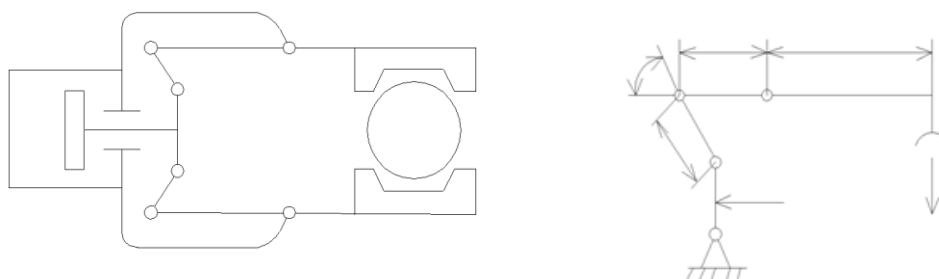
Конструктивна (а), розрахункова (б) схеми важільного механізму.
